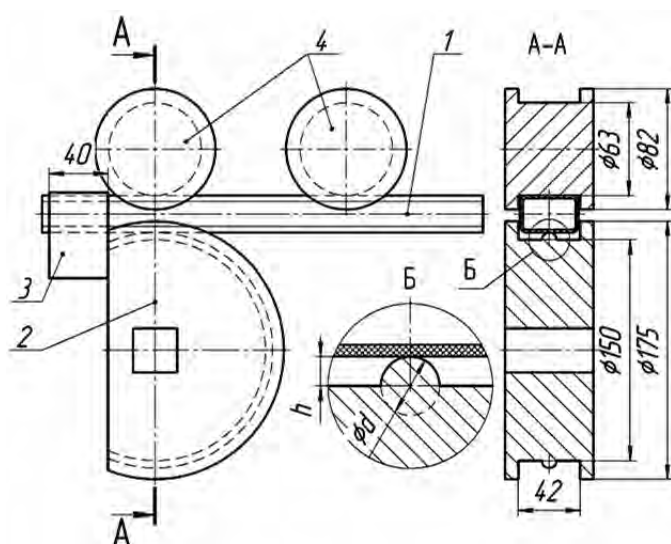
Схема способа гибки стальных прямоугольных труб в трубогибе с проточкой специального профиля на фасонном валке
